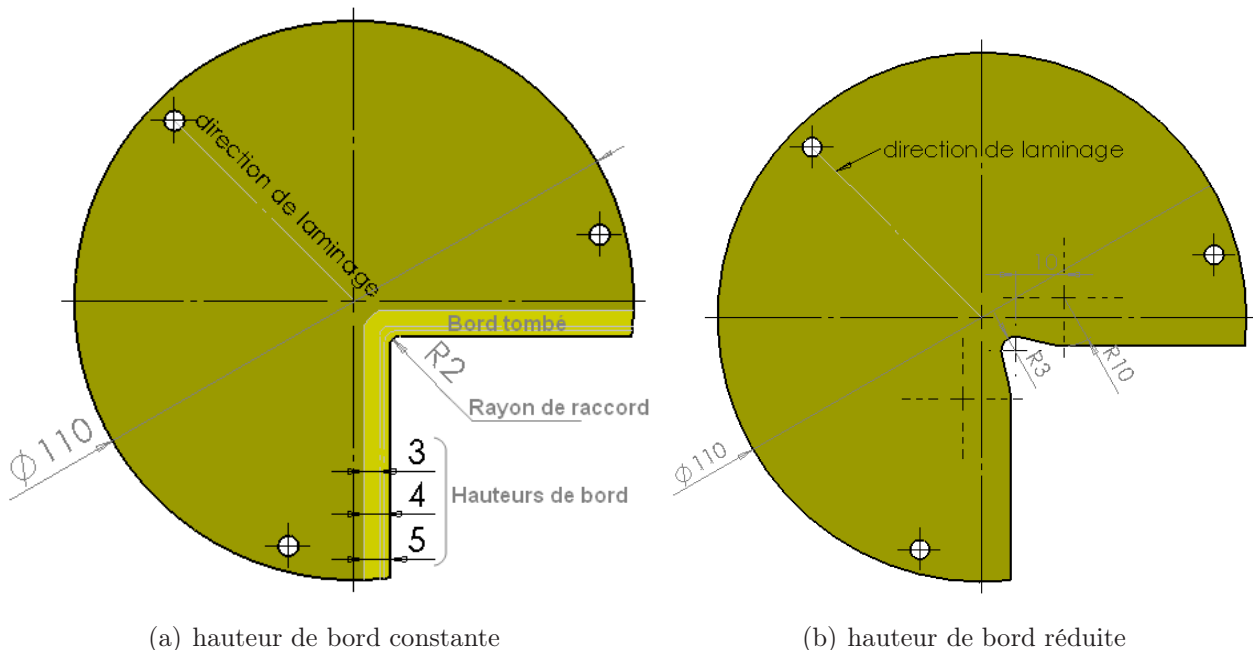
Géométries des éprouvettes de tombage (dimensions en mm)
